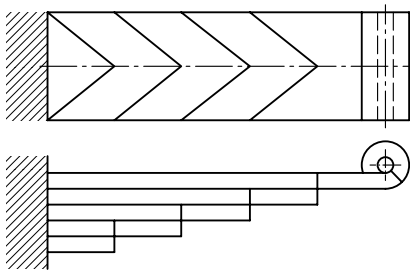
edS) geschichtete Blattfeder, rechteckige Ausführung
